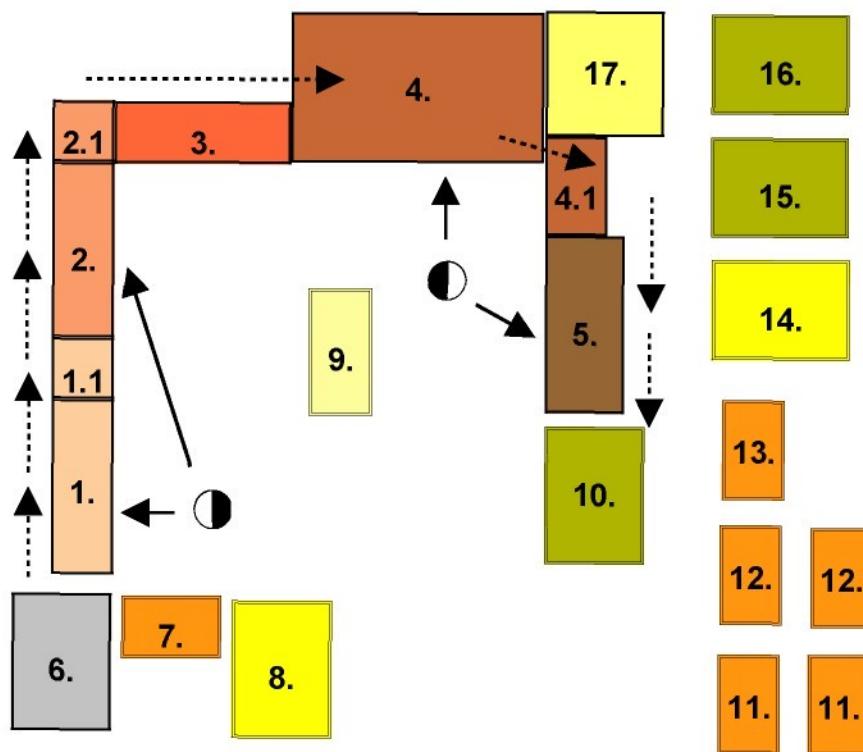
Dispozice montážního pracoviště L-420 pro výrobky 703-0044,
